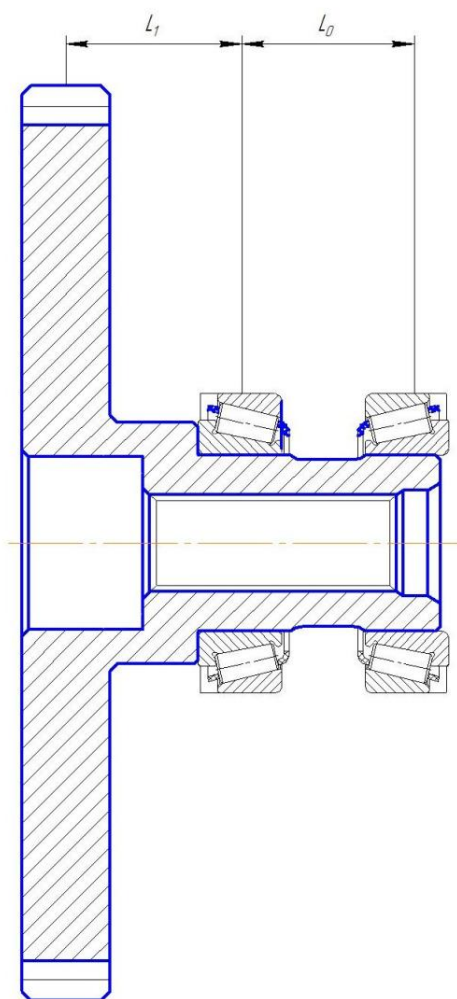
Компоновка ведущего вала заднего колесного редуктора
